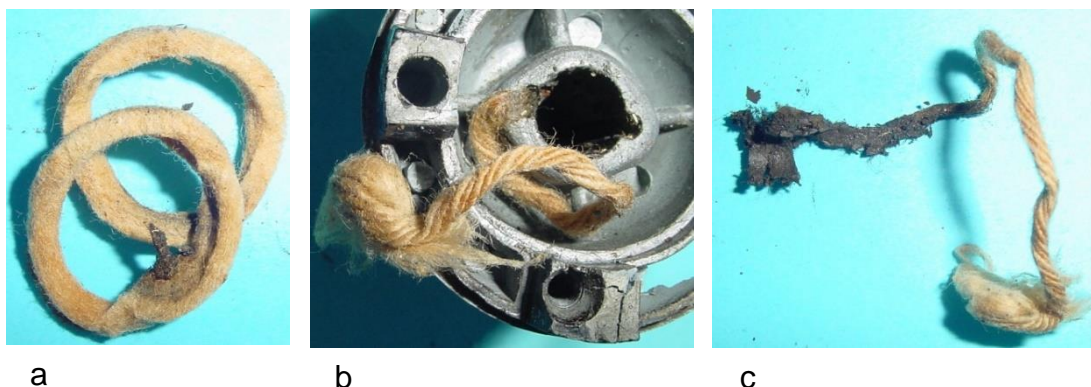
Elemente der Öldepots: a) Filzbandwindungen im Öldepot, b) Eingelegtes Verbindungsband, c) Separates Verbindungsband
